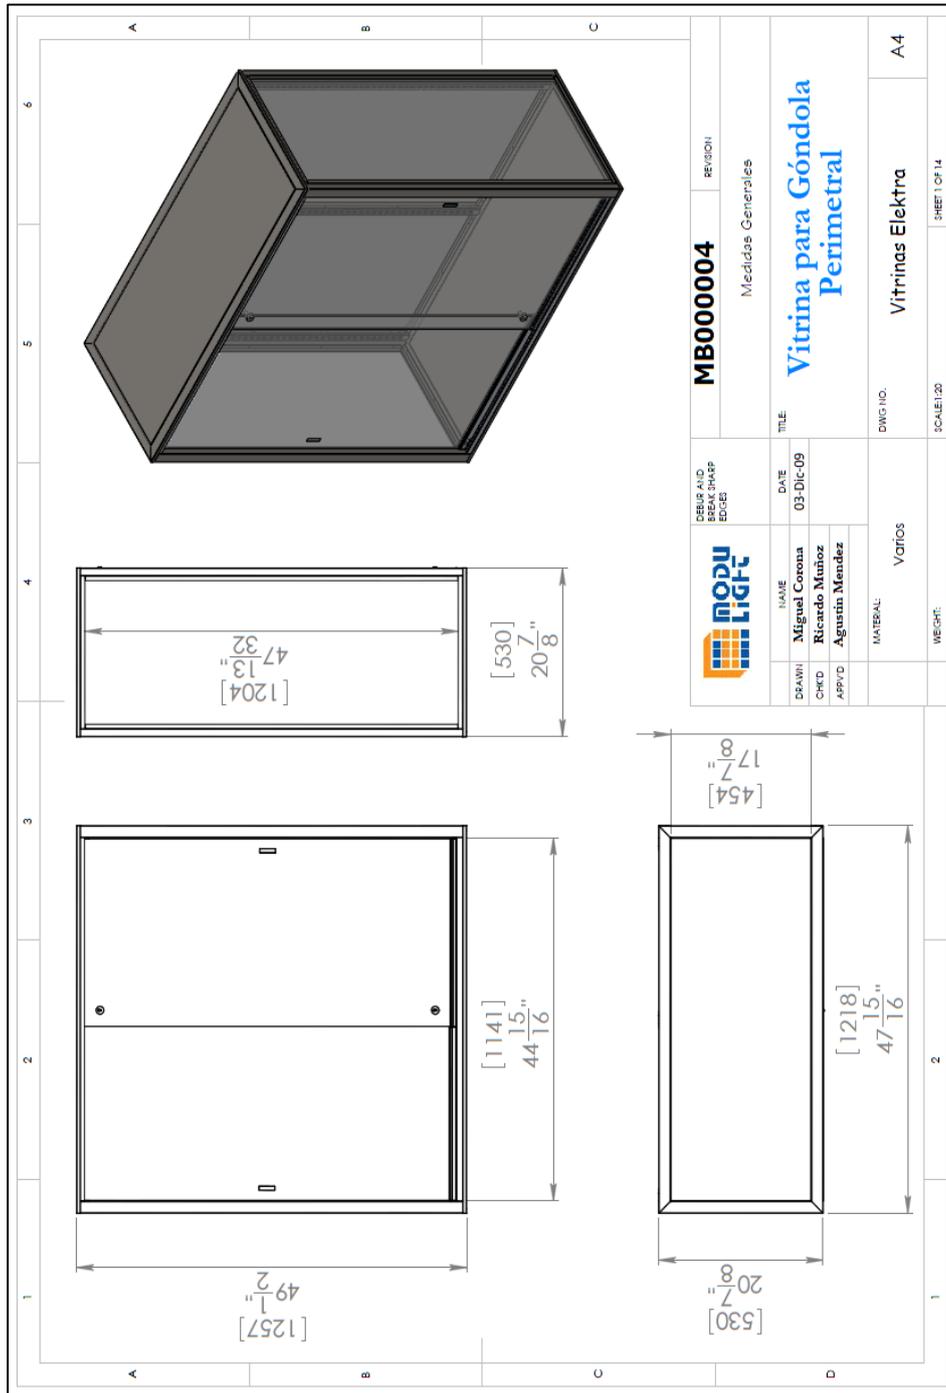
PLANO DE FABRICACIÓN DE VITRINA
